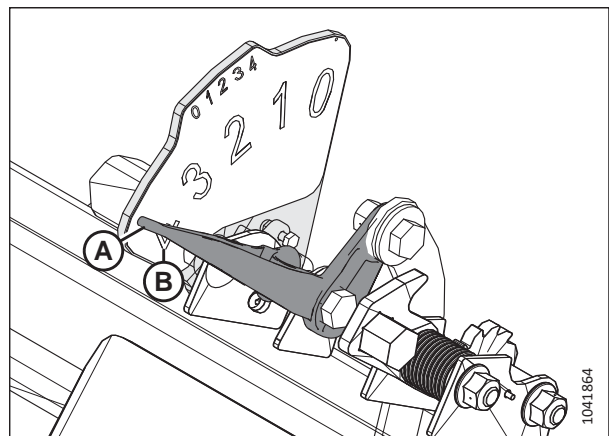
Auflagedruckanzeige links – Ansicht von hinten
